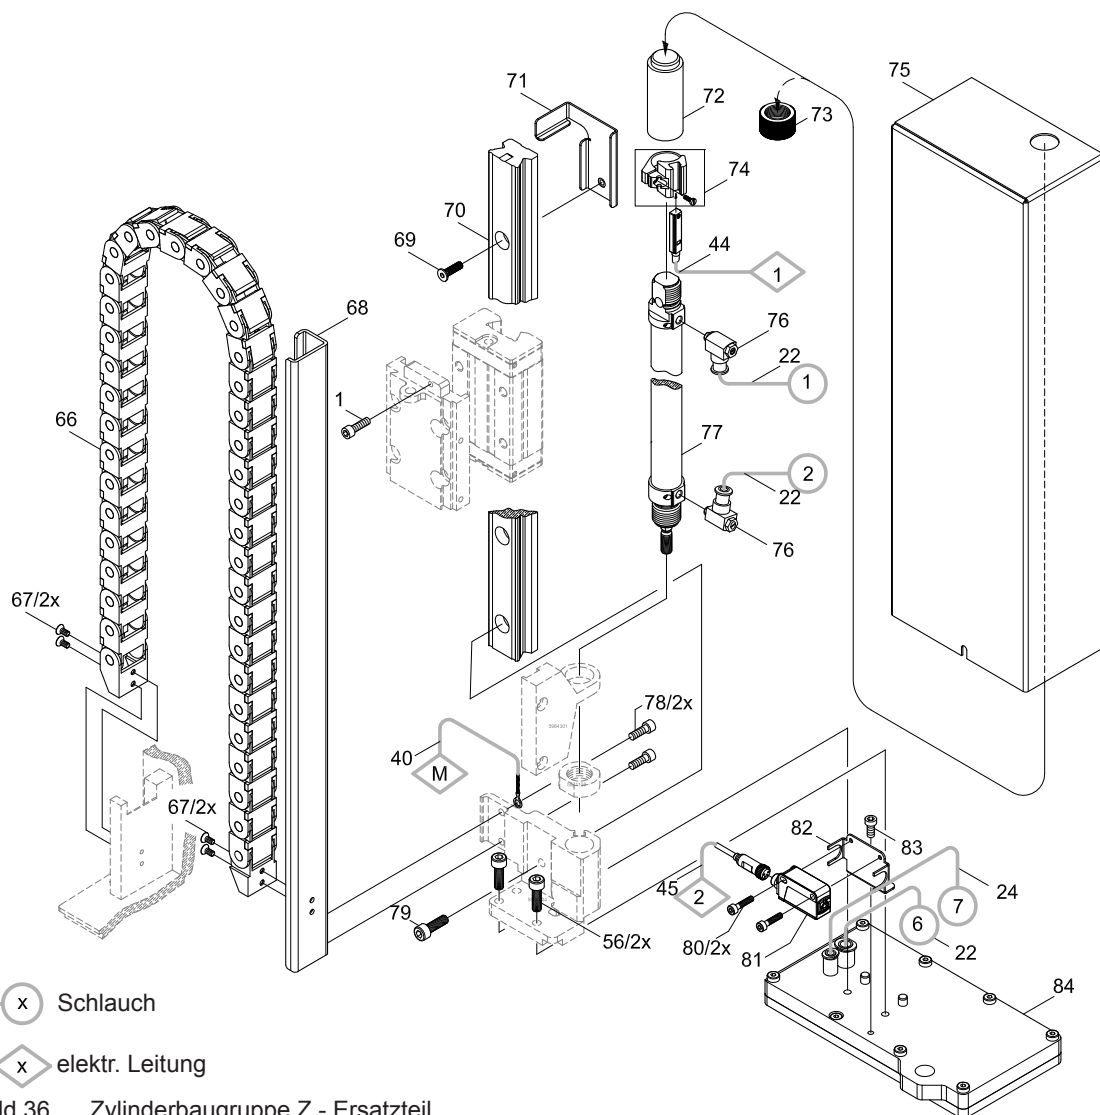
Zylinderbaugruppe Z - Ersatzteil
